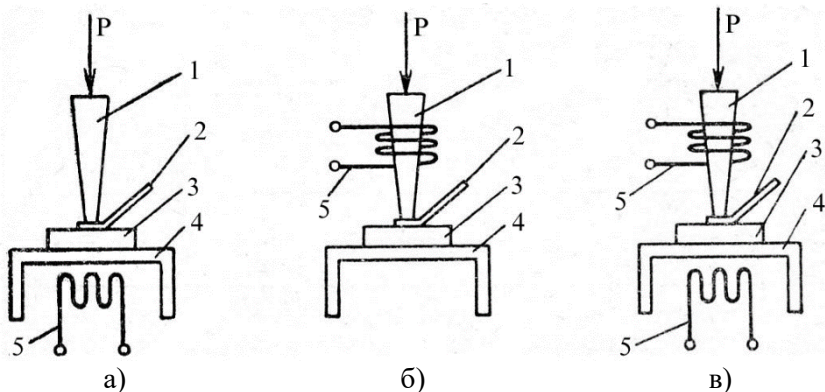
Разновидности термокомпрессии в зависимости от способа нагрева: а – нагрев только рабочего столика; б – нагрев рабочего инструмента; в – одновременный нагрев рабочего столика и инструмента; 1 – рабочий инструмент (пуансон); 2 – присоединяемый проводник; 3 – подложка или кристалл ППИ; 4 – рабочий столик; 5 – спираль для нагрева
